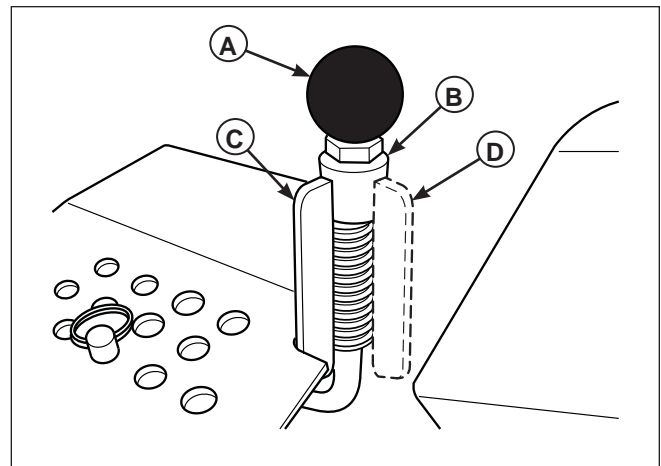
Fonctionnement de la plaque de condamnation de levier de verrouillage de levage de plateau de coupe
